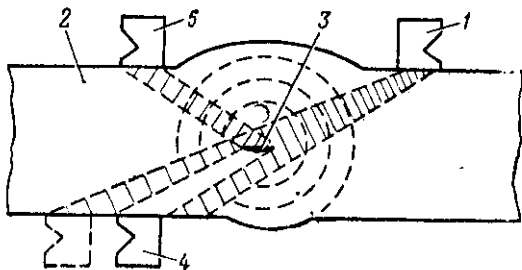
Схема ультразвукового контроля сварки:
